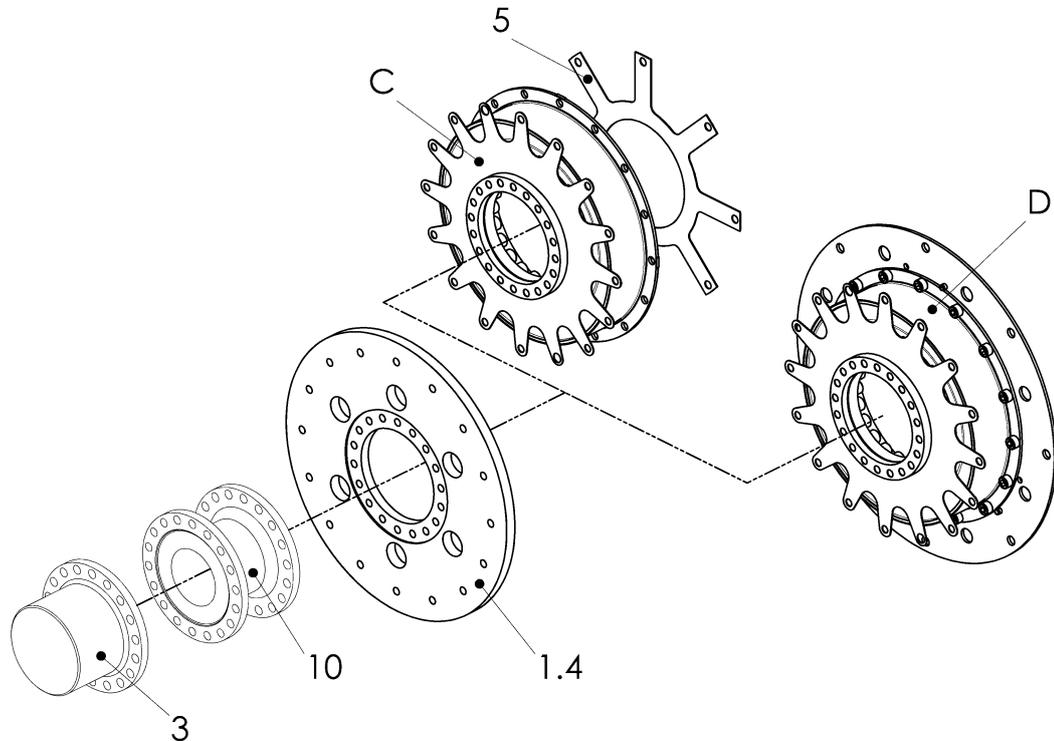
Beispiel: 033N-00035...00075-F.00
